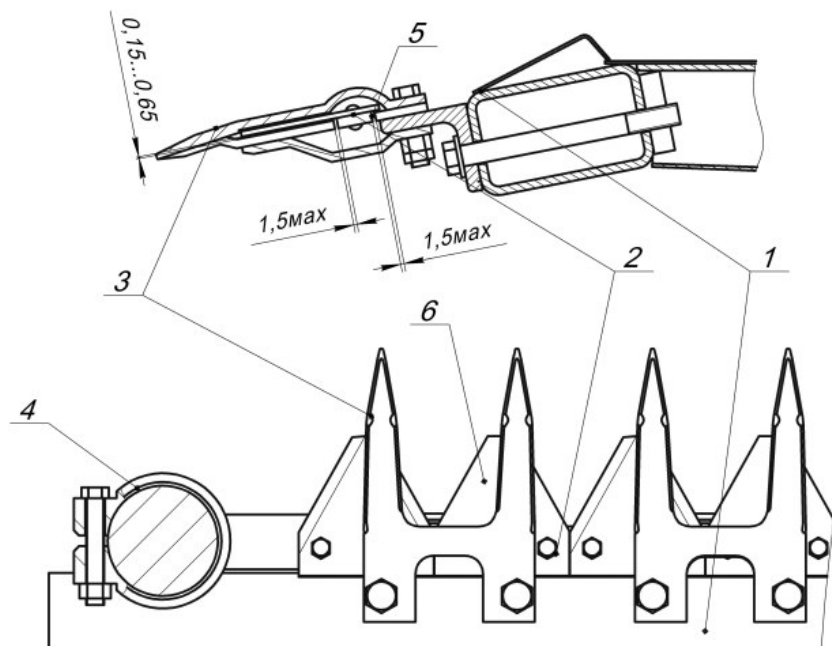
Режущий аппарат: 1 – пальцевый брус; 2 – нож; 3 – сдвоенный палец; 4 – головка ножа; 5 – спинка ножа; 6 – сегмент.
